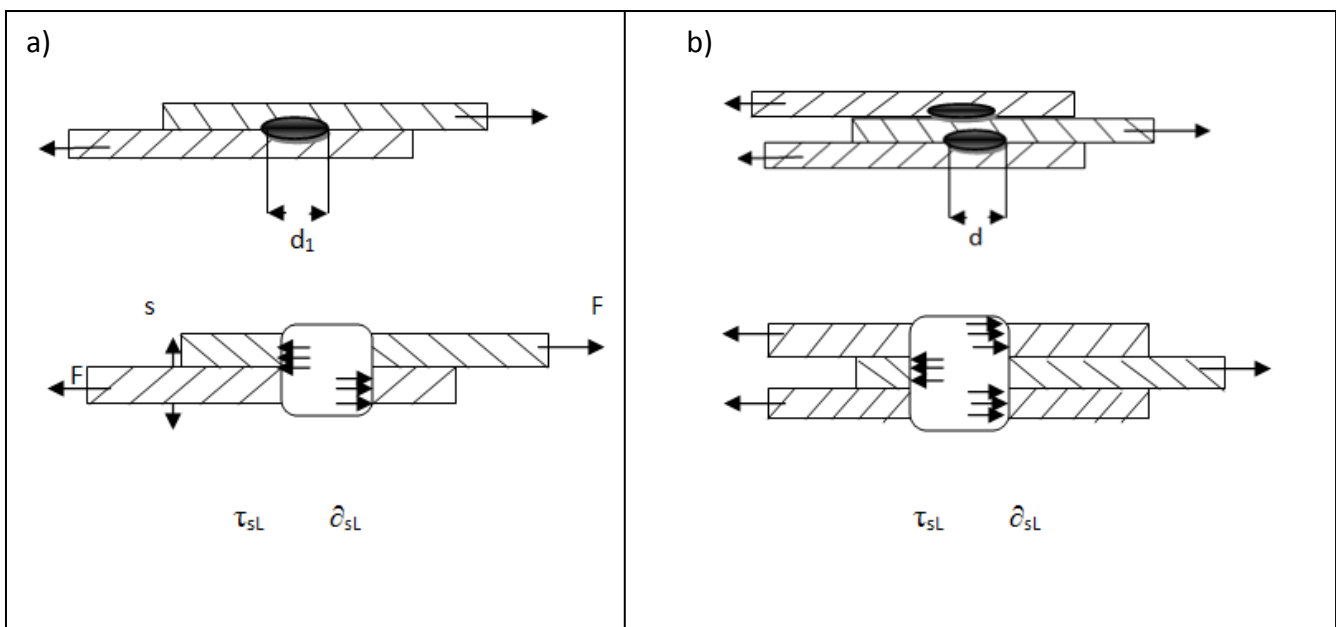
Calcul de l'assemblage soudé par point a) simple recouvrement b) double recouvrement [16].
